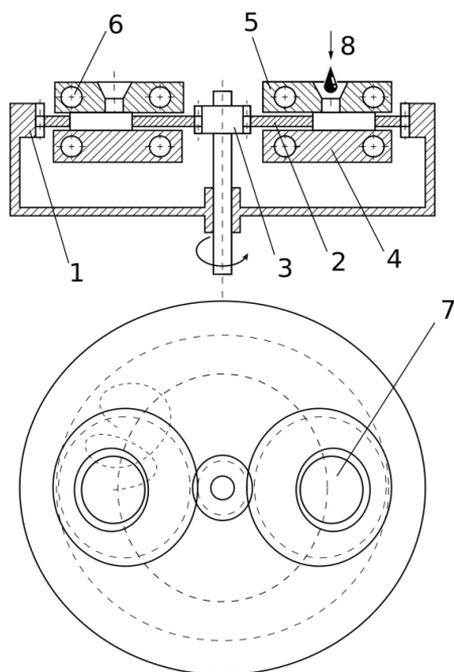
Станок двухстороннего шлифования: 1- внешняя шестерня; 2 – сепаратор; 3 – внутренняя шестерня; 4 – нижний шлифовальный; 5 – верхний шлифовальный; 6 – внешняя шестерня, 7 – обрабатываемые пластины, 8 - подача абразивной суспензии.
